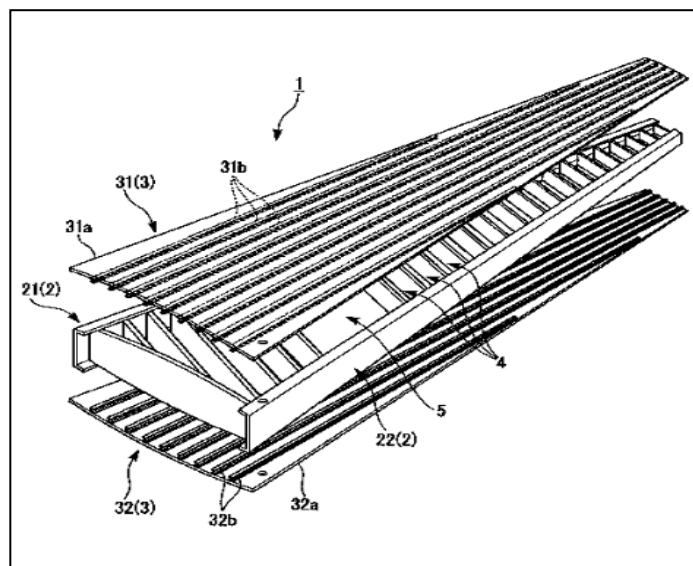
Vista en perspectiva del despiece ordenado de una configuración esquemática de un ala principal. Fuente: WO2012121322
